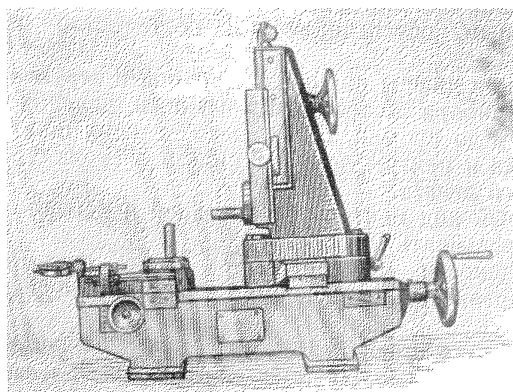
Межцентромер с кронштейном для проверки конических колес
